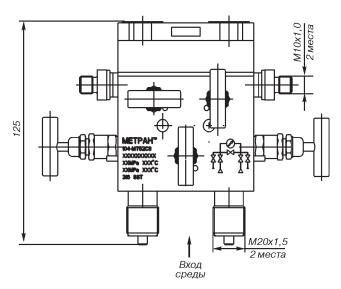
5-вентильный блок модели 0104 М Т 5 с кодом соединения с процессом С. Габаритные и присоединительные размеры см.рис.5.
